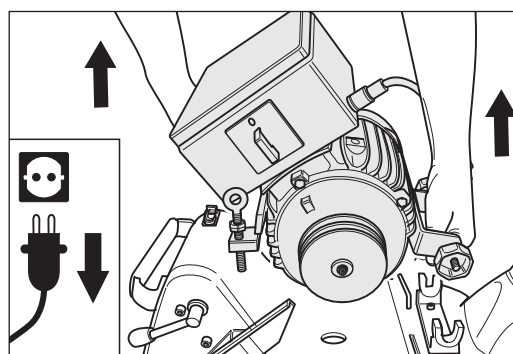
Den Motor vom Maschinengehäuse abnehmen.
